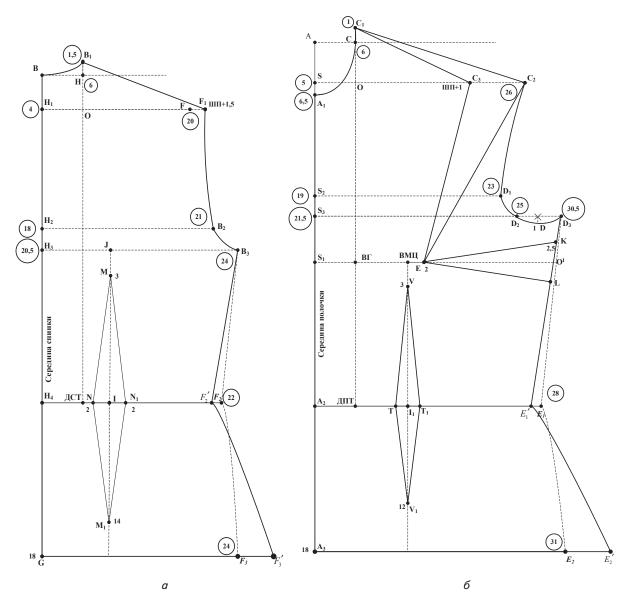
Ілюстрація уточнення креслень: a — креслення спинки;  $\delta$  — креслення полочки
